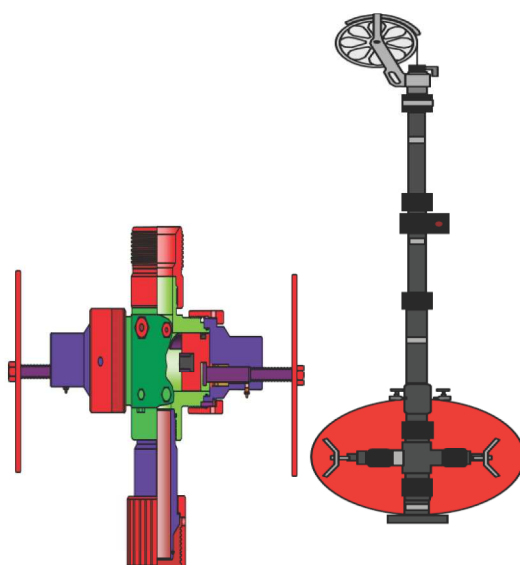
Wire-line surface equipment: dettaglio del primo blocco di sicurezza a testa pozzo.
